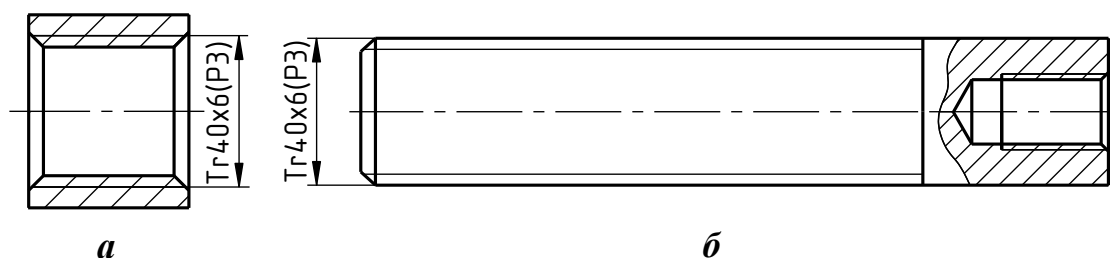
Обозначение трапецидальной ходовой резьбы и указание ее основных параметров на чертежах деталей винтовой передачи: а – внутренней резьбы в отверстии внешней детали (гайки); б – наружной резьбы на внутренней детали (винте)
